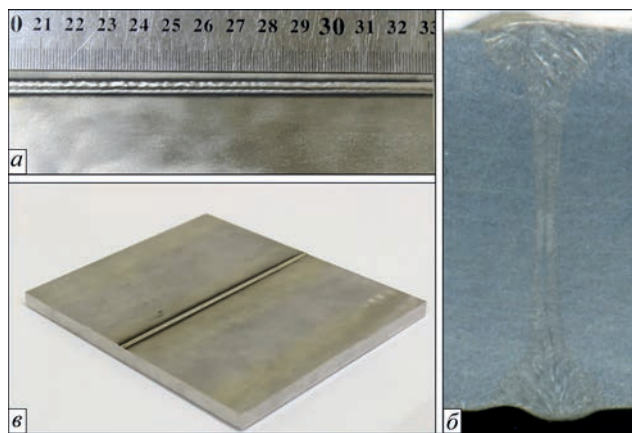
Двопрхідне гібридне зварювання пластин AISI304 ($\delta = 10$ мм): а – зовнішній вигляд шва; б – поперечний перетин; в – зовнішній вигляд зварного з'єднання
